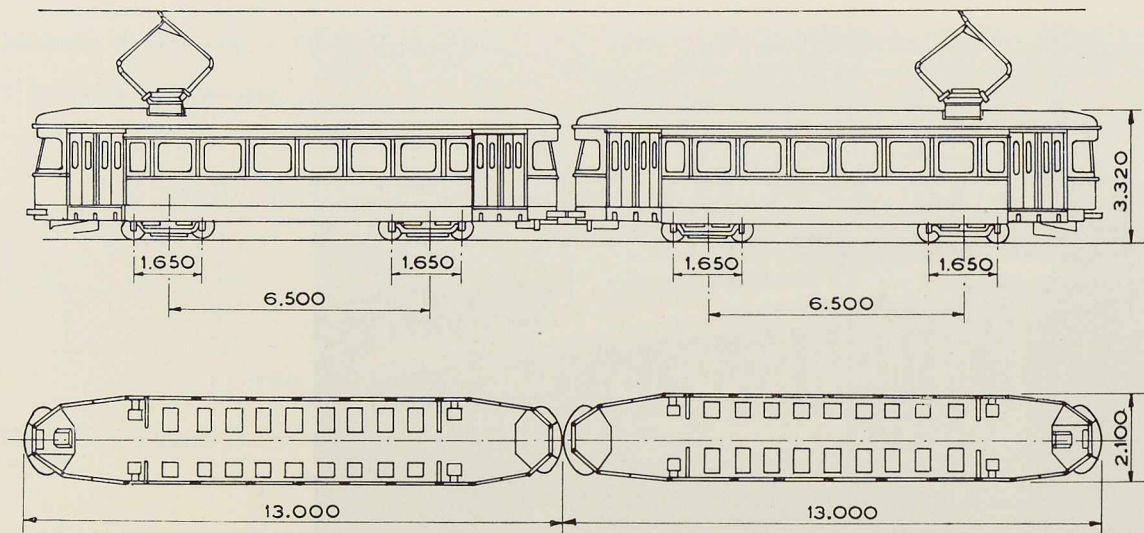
Elévation et plan d'une rame de voitures type 500.
